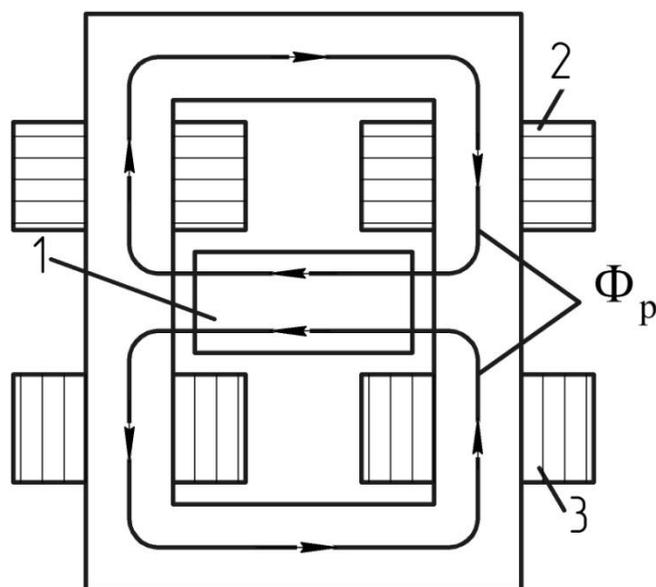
Сварочный трансформатор с подвижным шунтом (схема):
